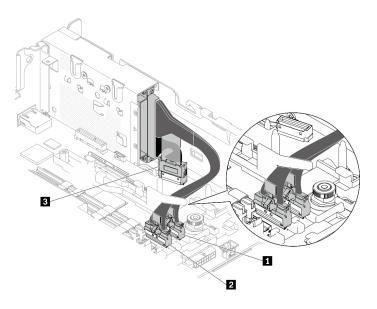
Roteamento de cabos do adaptador Ethernet OCP 3.0
